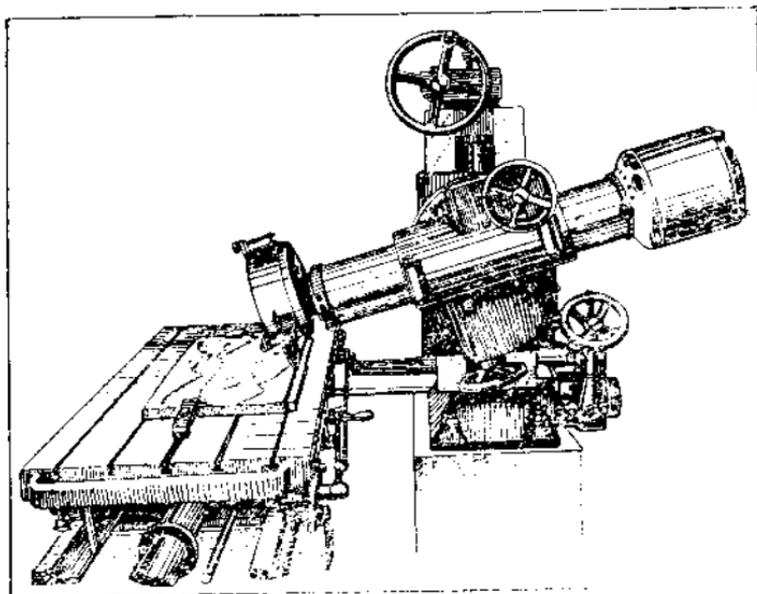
Универсальный фрезерный станок для производства реза под любым углом
